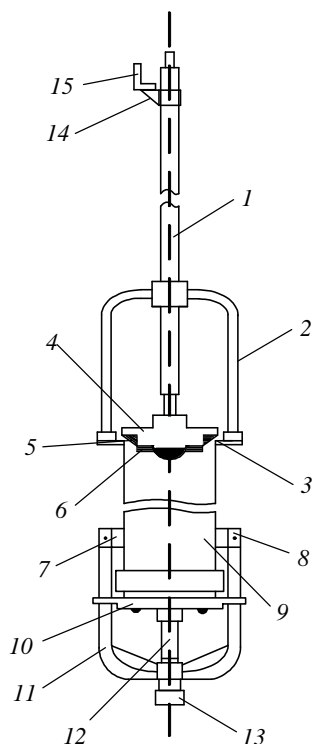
Универсальный сливной прибор с двумя независимыми затворами: 1 – упорная штанга; 2 – стойка; 3 – седло стойки; 4 – корпус клапана; 5 – уплотнитель резиновый; 6 – прижимная крышка клапана; 7 – бонка; 8 – валик скобы; 9 – патрубок; 10 – нижняя крышка; 11 – скоба; 12 – винт нижней крышки; 13 – рукоятка; 14 – кронштейн; 15 – уголок
